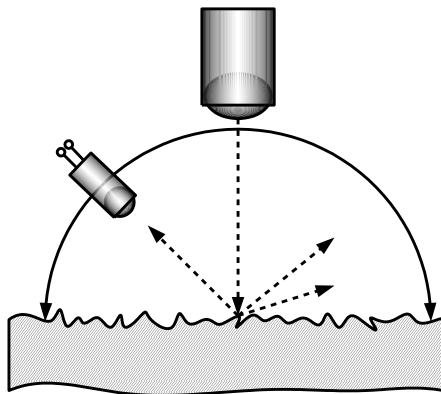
Схема дії лазерного оптичного фоторезисторного перетворювача
